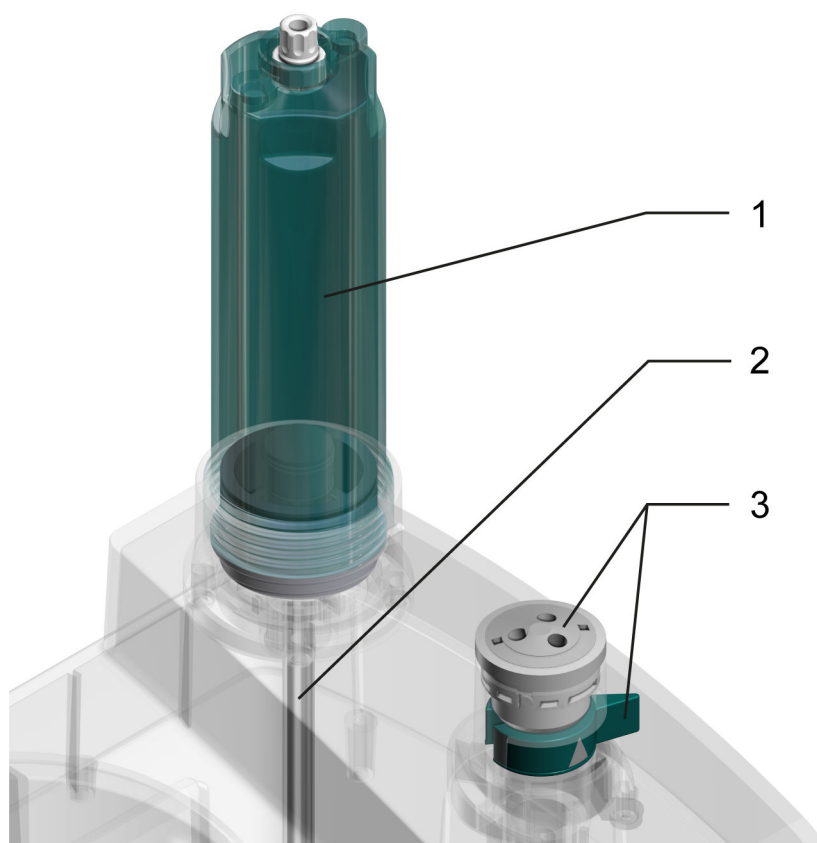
Unidad de cilindro y motor de dosificador – Visión conjunta
